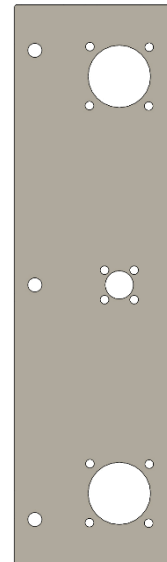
'de PCB' nin bağlanacağı tablanın boyutları ve üstten görünümü yer almaktadır. Bu tablanın üzerine bir çift taraflı bant ile PCB yapıştırılacak ve kart işlenecektir. Tablaya bağlayabileceğimiz en büyük boyut 215 mm x 130 mm aralığındadır. Bu tabla ile 200 mm x 100 mm boyutlarında bir PCB rahatlıkla işlenebilmektedir. Genellikle prototip basımında kullanılan en büyük boyut 100mm x 100mm olduğu düşünülerek tablo boyutu bu oranda tasarlanmıştır. İhtiyaç olduğu takdirde tablo boyutu 200mm'e kadar aynı tasarım üzerinde genişletilebilir.
